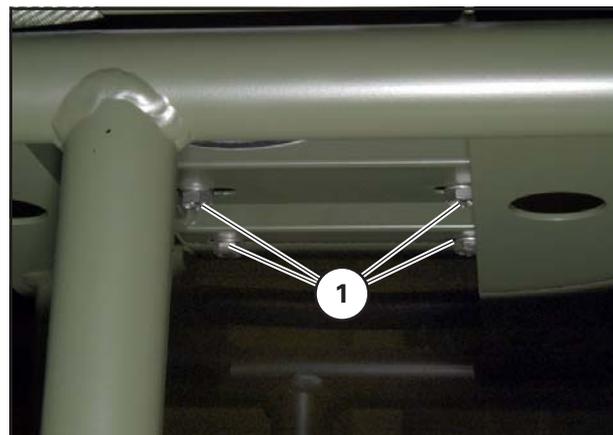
Befestigungsschrauben Wasserpumpe (Unterseite JSTDS-SSL)
